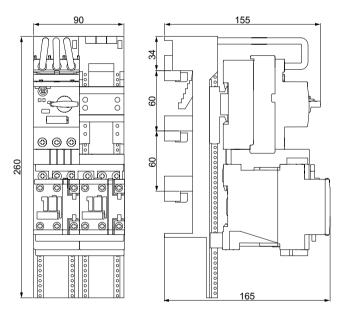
Arrancador inversor S0/S0 y S00/S0, DC, bornes de tornillo 3RA2220-..D..-0BB4
